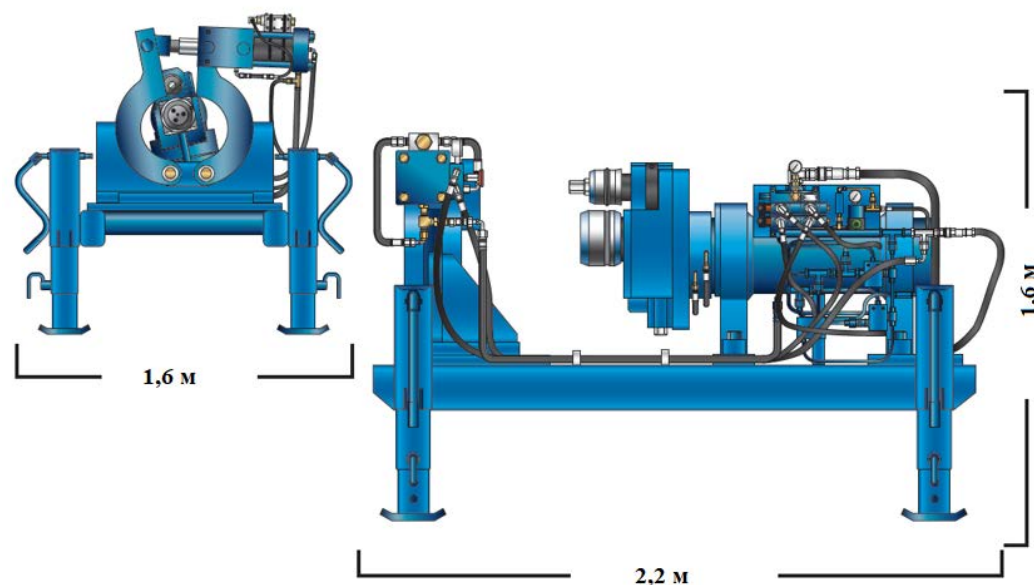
Оборудование для подготовки штифтового конца труб 8000-12
